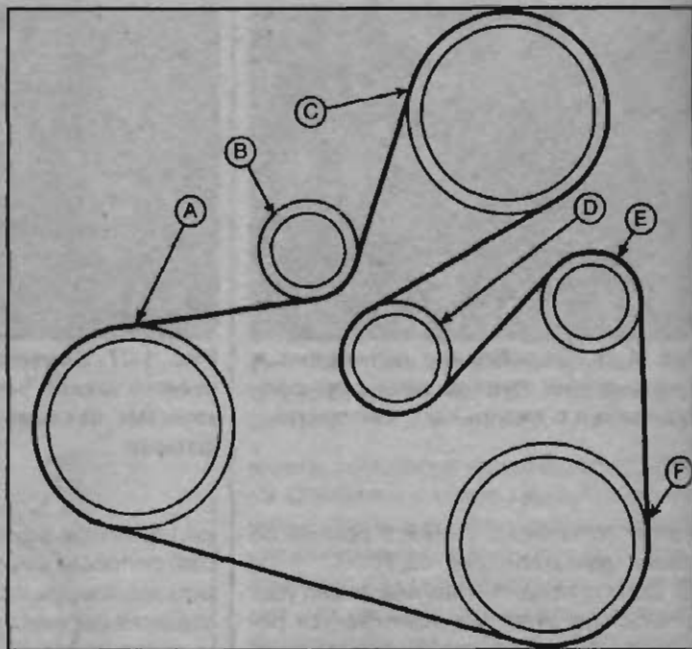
Расположение ремня привода навесных агрегатов на шкивах дизельного двигателя с системой кондиционирования воздуха: А – шкив коленчатого вала; В – шкив автоматического механизма натяжения ремня; С – шкив насоса усилителя рулевого управления; D – эксцентриковый шкив механизма натяжения; Е – шкив генератора; F – шкив компрессора системы кондиционирования воздуха
